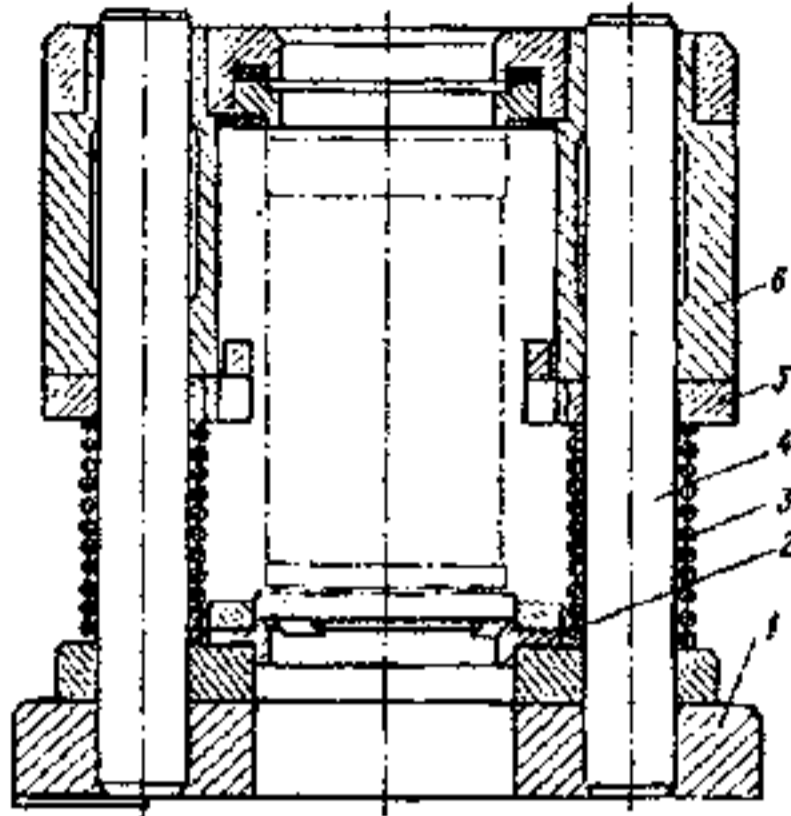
Затискний пристрій для встановлення гільзи циліндра під час розточування: 1 - станина; 2 - упорне кільце; 3 - пружина; 4 - напрямна колонка; 5 - шип; 6 - напрямна втулка
